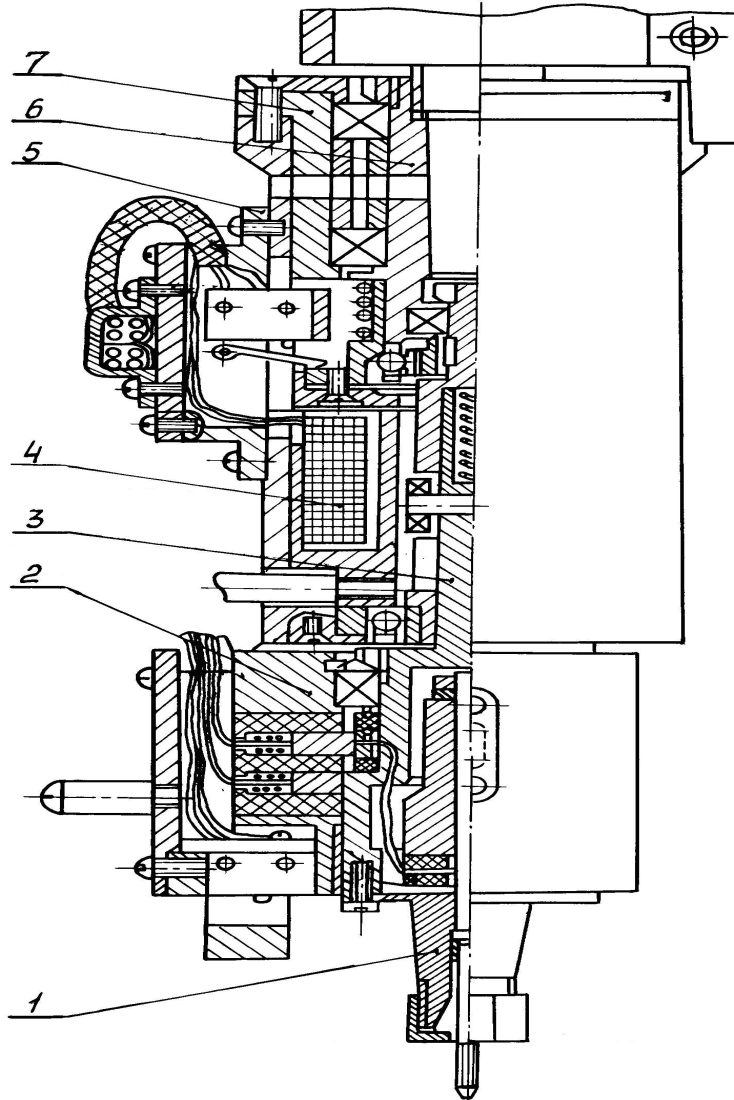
Ультразвуковое устройство, применяемое для нарезания резьб М2-М6 в глухих отверстиях: 1 - концентратор; 2 – корпус; 3 – ведомый вал; 4 – обмотка электромагнитной муфты; 5 – корпус; 6 – ведущий вал; 7 – втулка.
